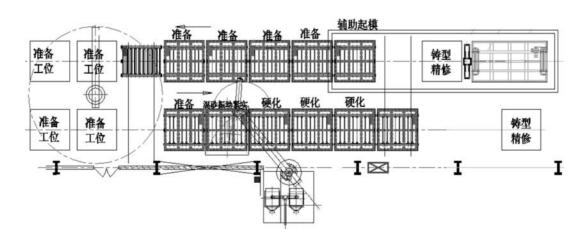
典型铸型快速造型系统工位设计布局 Fig. 3 The layout of typical casting rapid prototyping system
